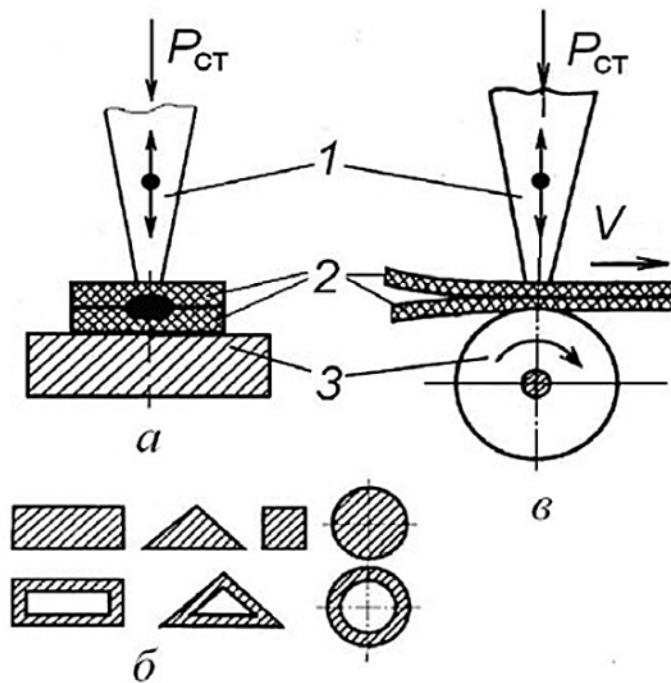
Схеми ультразвукового зварювання в ближньому полі: а – пресове; б - можлива форма робочого торця хвилеводу при пресовому зварюванні; в – шовна; 1 – хвилевід; 2 - зварювальні деталі; 3 – опора.
